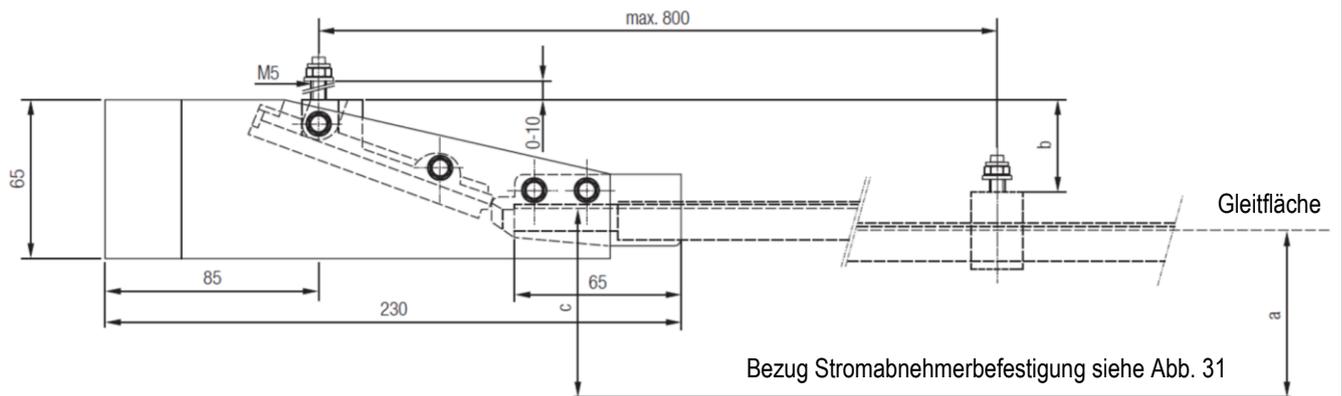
Einfahrtrichter 081182 – kurze Ausführung
